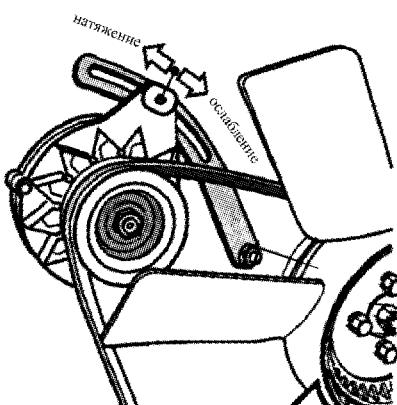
8 Проверка и регулировка резинового ремня вентилятора
